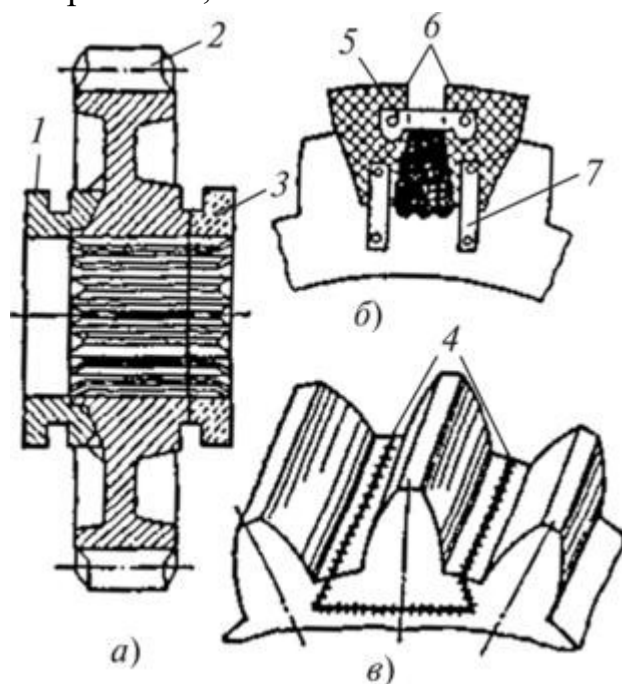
Схемы ремонта зубчатых колес: *а* — привариванием кольца; *б* — наплавкой зуба по медным шаблонам; *в* — приваркой вкладыша; 1 — кольцо; 2 — зуб; 3 — удаляемая часть; 4 — сварные швы; 5, 7 — планки; 6 — медные шаблоны
